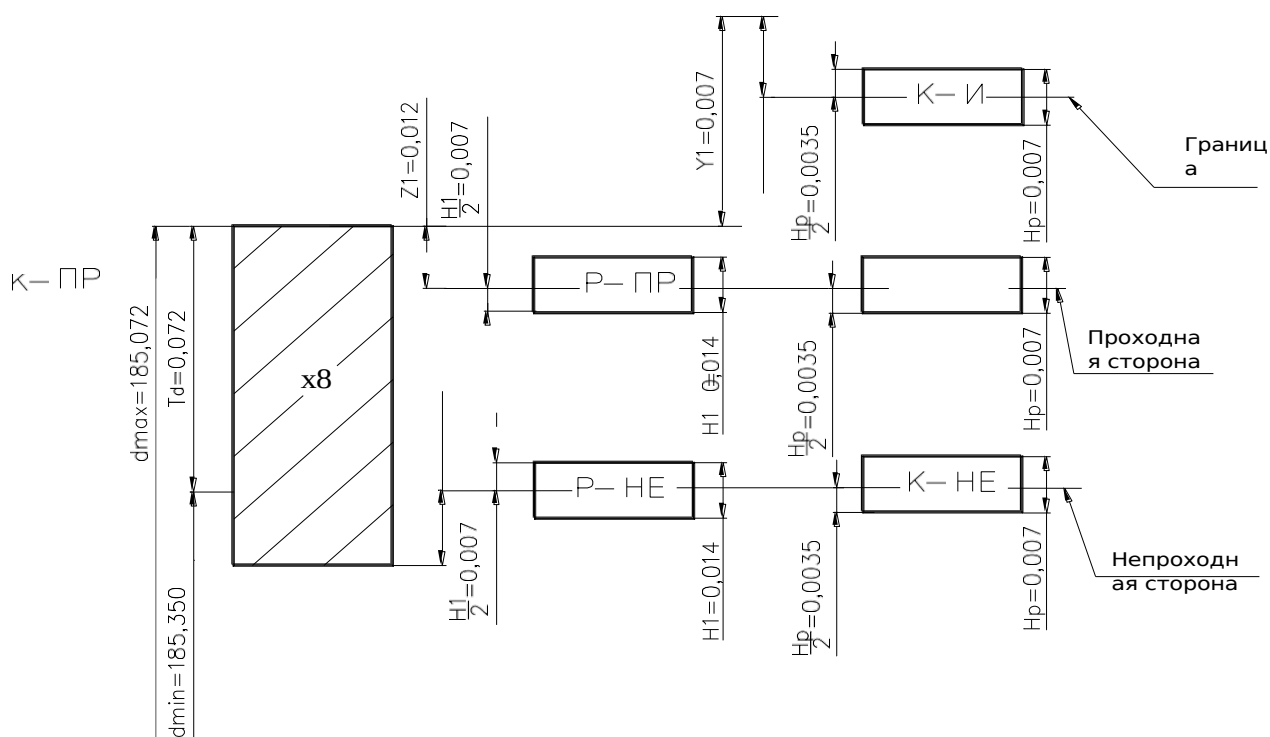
Схемы полей допусков для калибров-скоб
